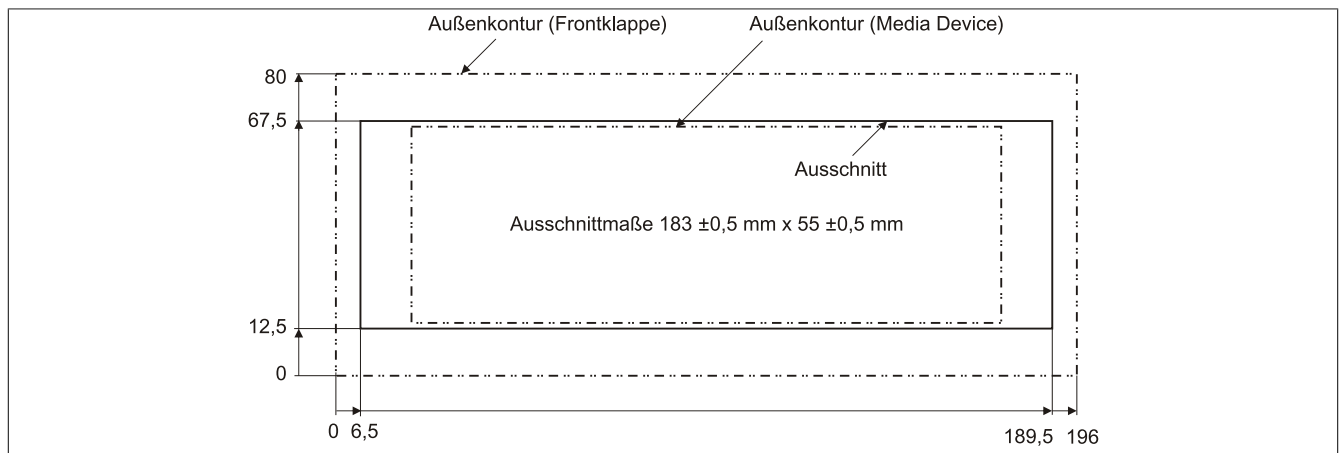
Einbauausschnitt USB Media Drive mit Frontklappe
